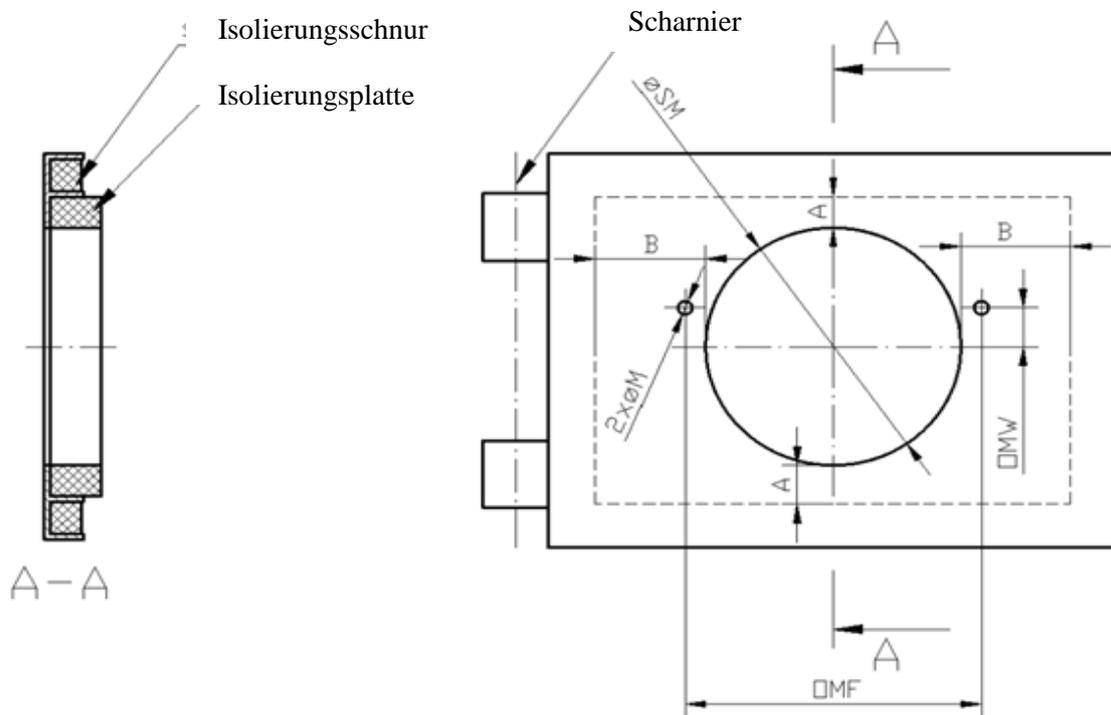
Schema der Herstellung von Montagebohrungen für Brenner mit einem Wärmedämmmantel und einer Montageplatte für Brenner: 4-16 kW, 5-20 kW, 6-26 kW, 8-36 kW
